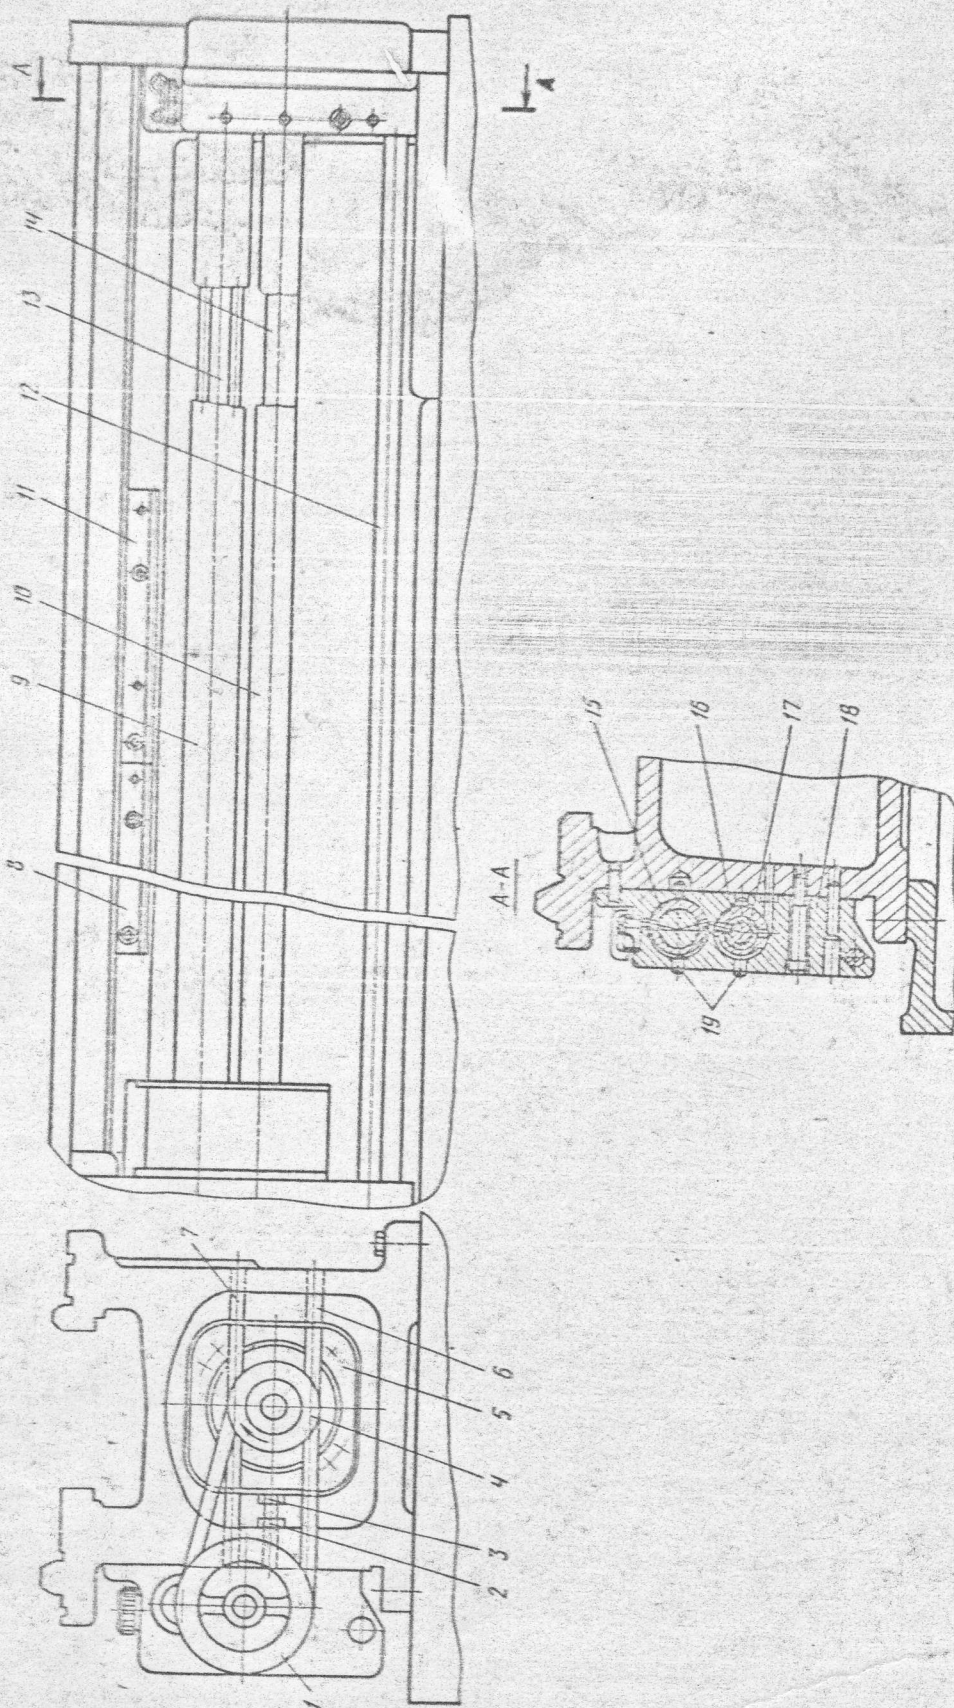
Станина, рейки, ходовой винт, ходовой вал и привод быстрых перемещений суппорта
